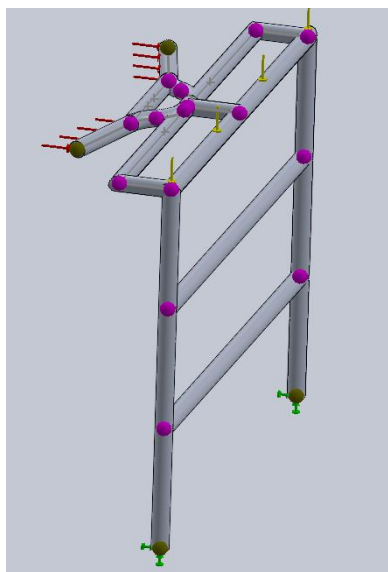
Detalle de las fuerzas consideradas en la simulación B.2 [fuente propia]
